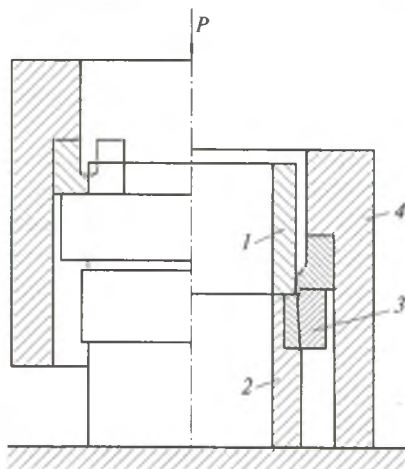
Схема изготовления титаноалюминиевого переходника холодной сваркой:
